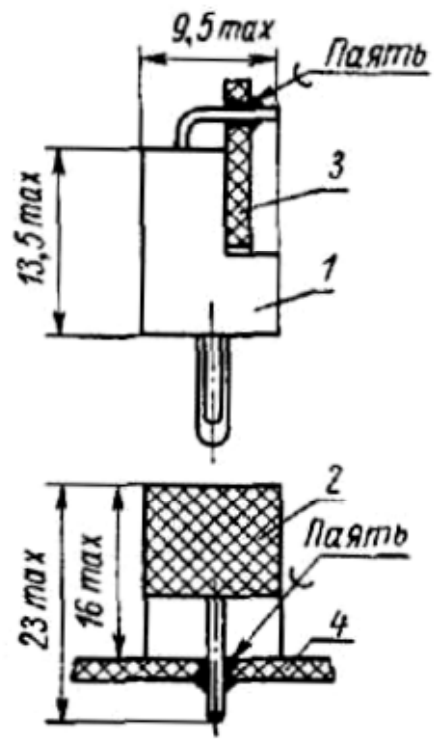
Установка разъёма ГРППЗ-24:
